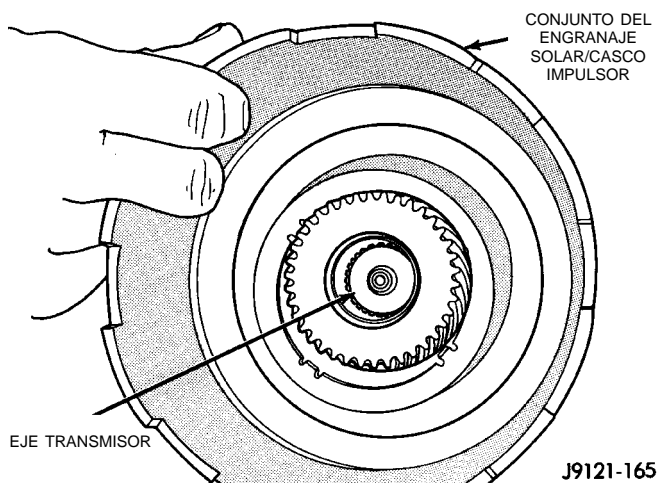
Instalación del engranaje solar y el casco impulsor ensamblados en el eje transmisor
